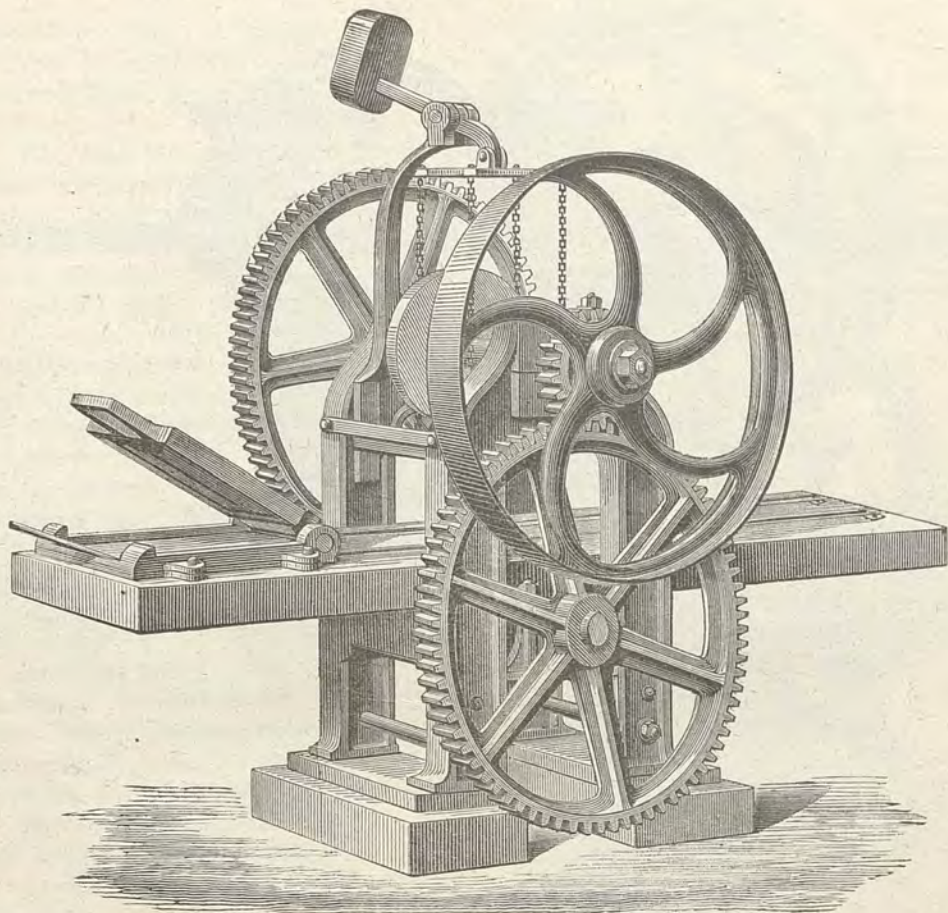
Macchina Boulet per impastare e formare tegole.
